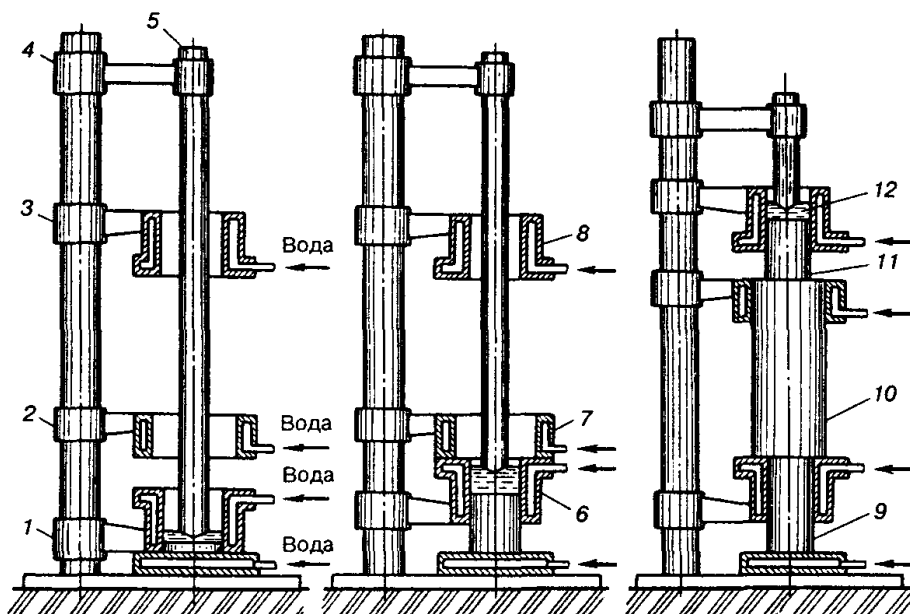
Схема виготовлення заготовки прокатного валка електрошлаковим литтям
